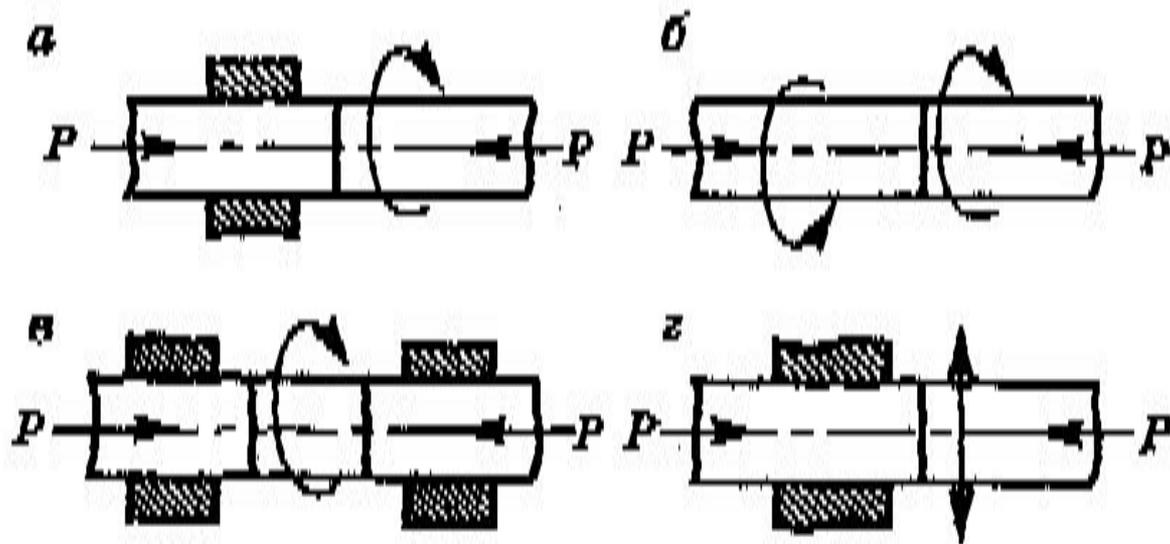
Принципиальная схема процесса сварки трением:
